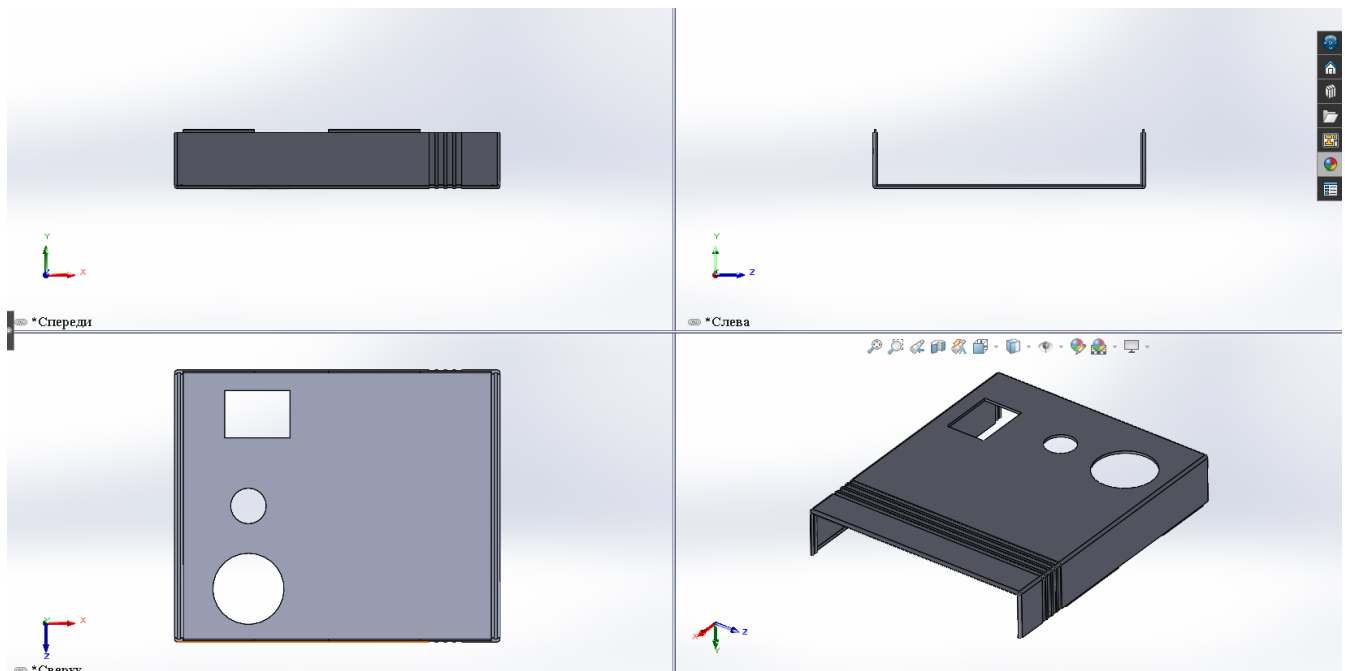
Тривимірна модель верхньої частини корпусу
